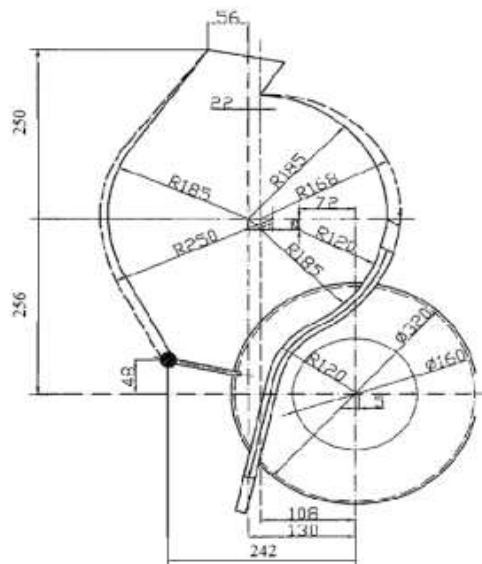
12. Профиль предлагаемой - новой формы рабочей камеры
